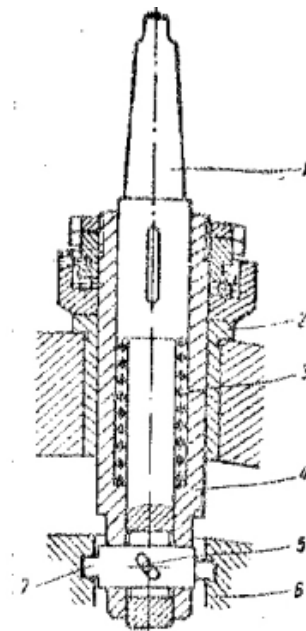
Приспособление для растачивания кольцевых канавок на сверлильном станке.
